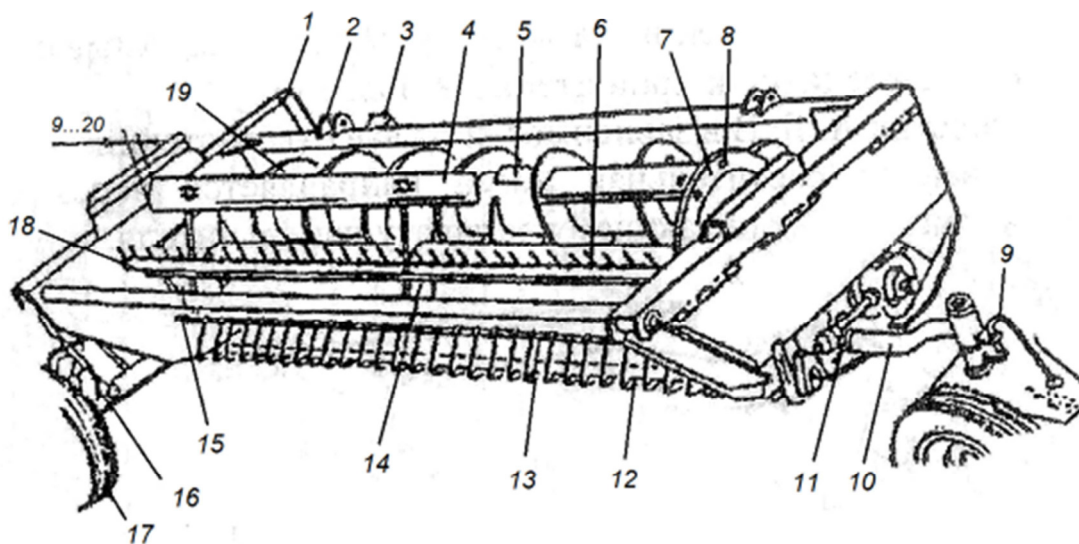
Жатка для трав: 1-рама; 2-ловители верхние; 3-редуктор контрпривода; 4-мотовило; 5-лопатка; 6-зуб пружинный; 7-дорожка; 8-отверстие монтажное; 9 и 11-фиксаторы передней тележки; 10-передняя тележка; 12-режущий аппарат жатки; 13-граблина; 14-держатель; 15-плита; 16-устройство натяжное задней тележки; 17-задняя тележка; 18-вал граблины; 19-шнec.
